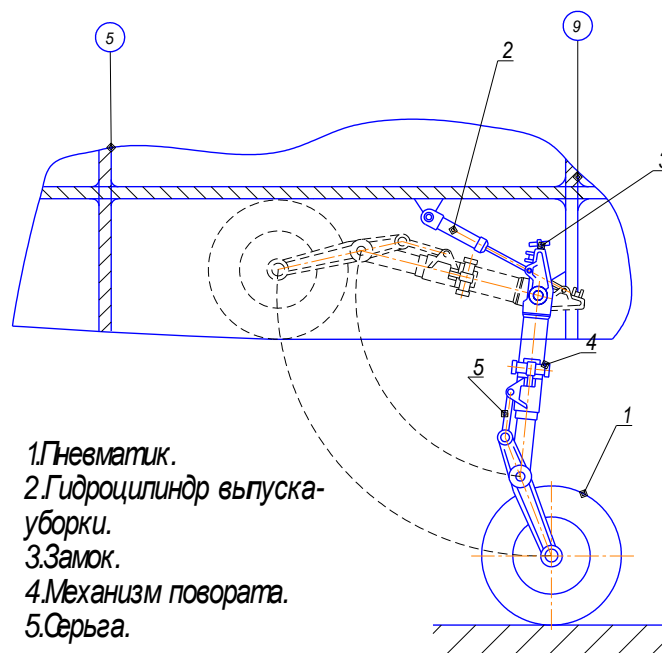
Конструктивно-силова схема носового стояка шасі.
